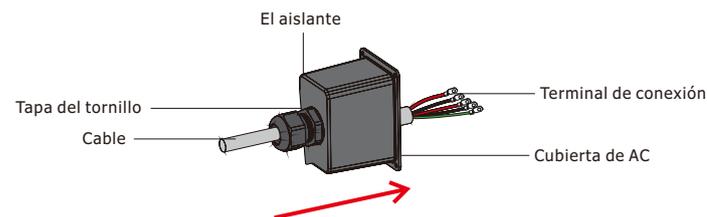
El cable de AC pasa a través de la cubierta del terminal
